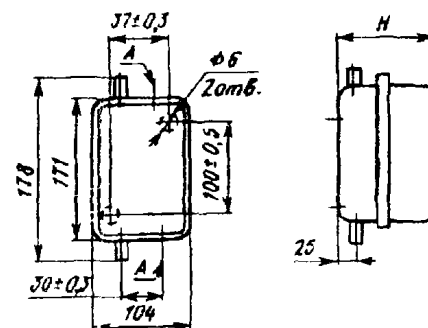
Габаритные, установочные размеры пускателей типа ПМ12-010 нереверсивных в оболочках степени защиты IP54
